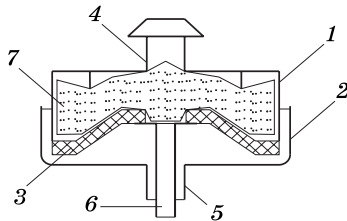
Капельница с прижимающимся поролоном (патент 2409023): 1 – верхняя часть корпуса; 2 – нижняя часть корпуса; 3 – резиновая прокладка; 4 – входной патрубок; 5 – выходной патрубок; 6 – внутренний выходной патрубок; 7 – поролон
